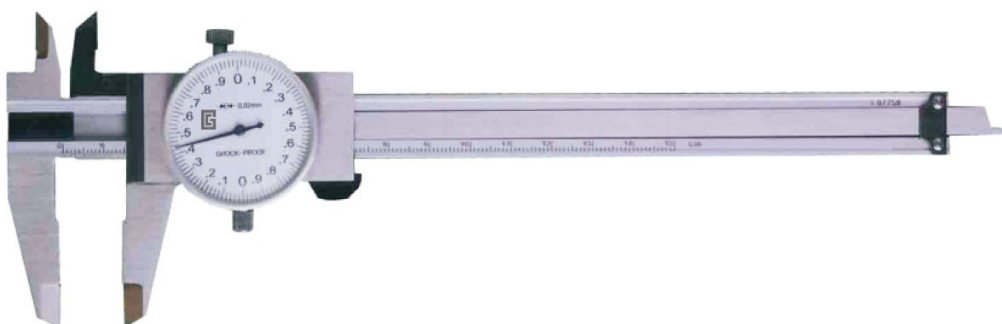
Общий вид штангенциркулей типа ШЦК-I.
